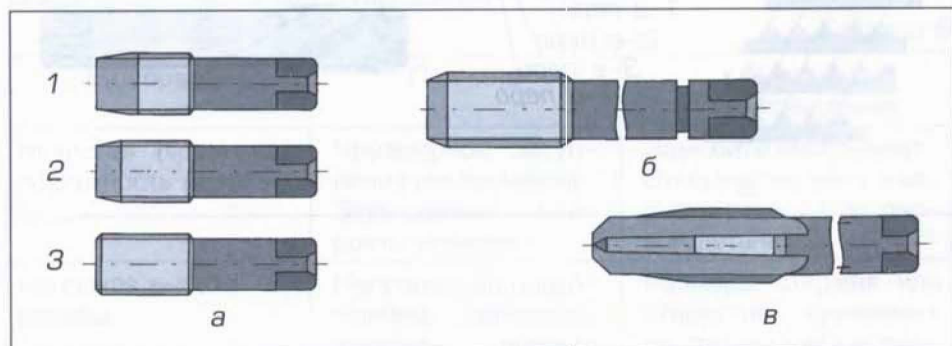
Метчики для нарезания внутренней резьбы на станке:
